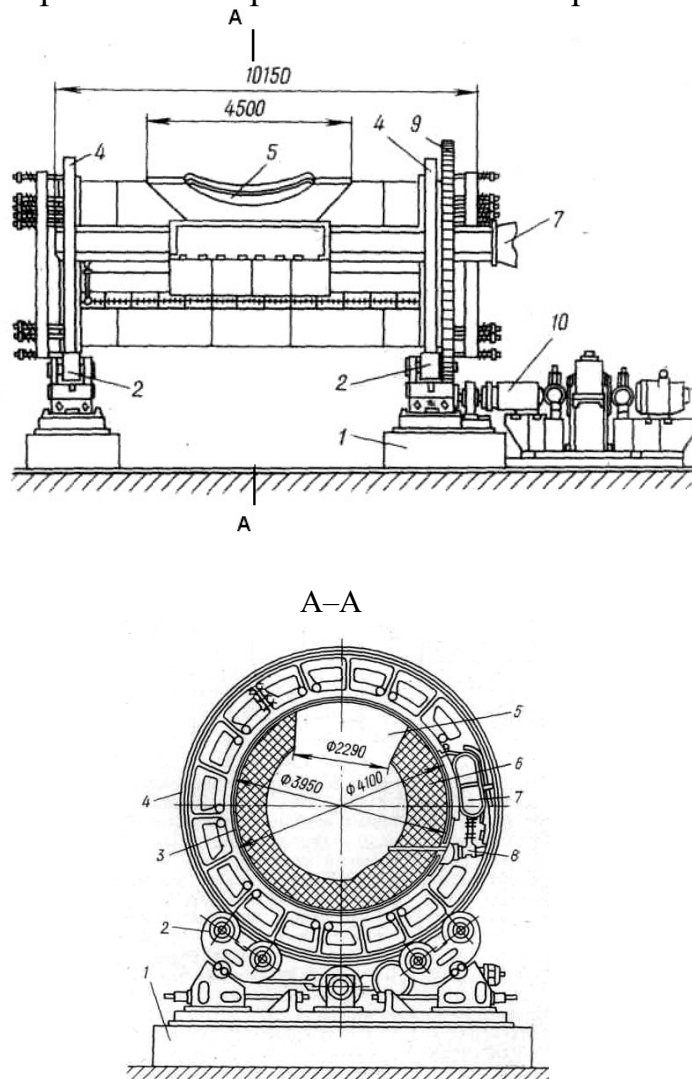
Конвертер для продувки штейнов: 1 – фундамент; 2 – опорные ролики; 3 – бочка; 4 – опорный обод; 5 – горловина; 6 – футеровка; 7 – воздушный коллектор; 8 – фурма; 9 – зубчатый обод; 10 – привод для вращения бочки
